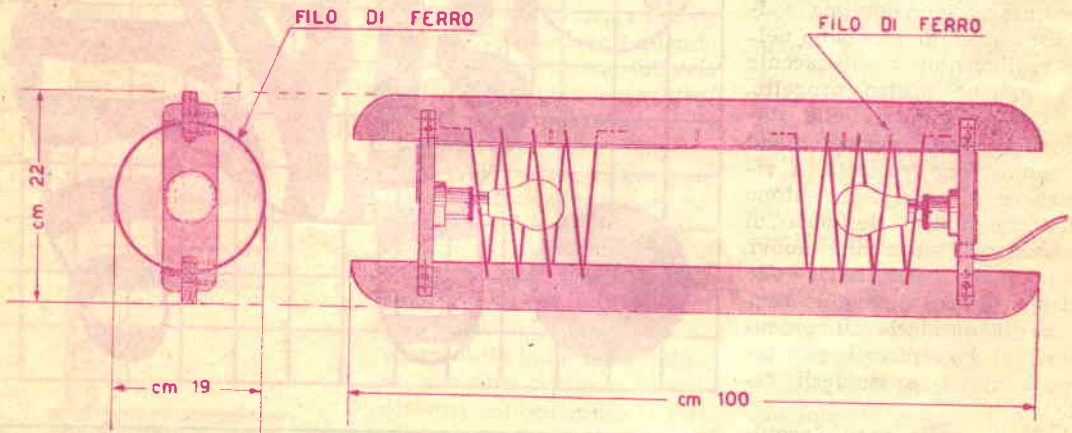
Questa, la disposizione delle lampadine nello scaldaletto. Si noti anche la disposizione del filo di ferro per la protezione.
